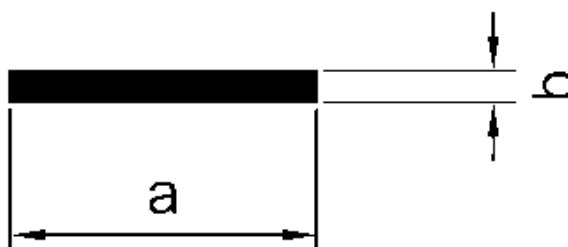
сварная лента «ПрофиБанд Welding Tape»
